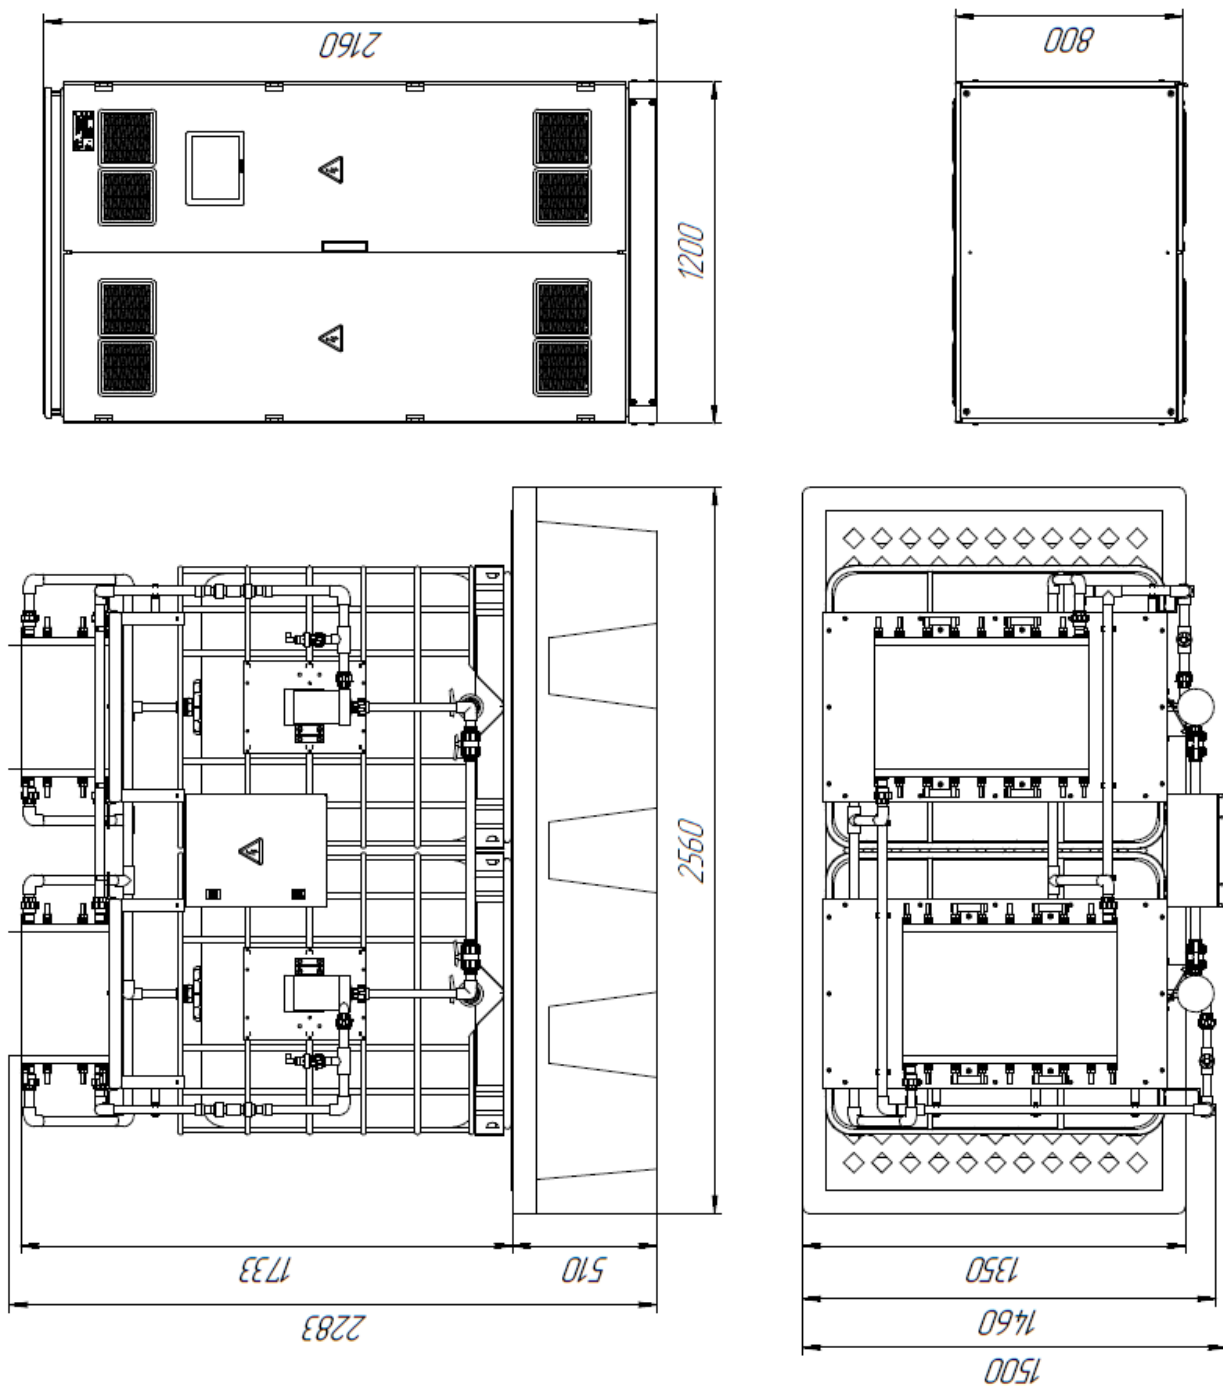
Габаритный чертеж и общий вид СБП-ПАКБ
